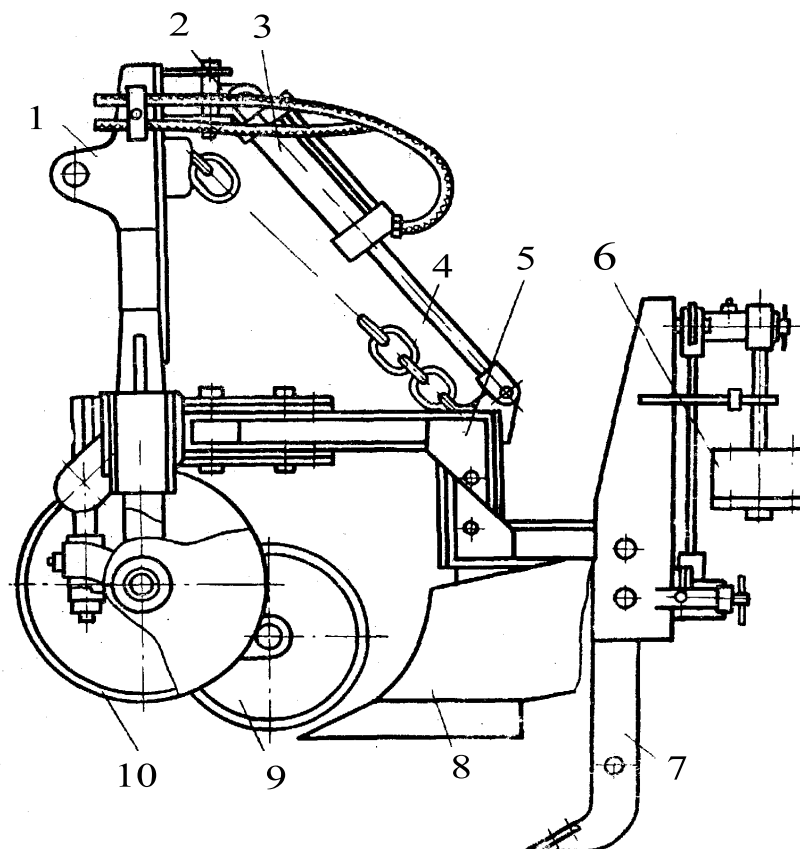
Плуг для склонов ПЛС-0,6: 1 – рама с навесным устройством; 2 – проушина; 3 – гидроцилиндр; 4 – цепь; 5 – рама подвижная; 6 – маятник; 7 – рыхлительная лапа; 8 – двухотвальный плужный корпус; 9 – дисковый нож; 10 – опорные колеса
